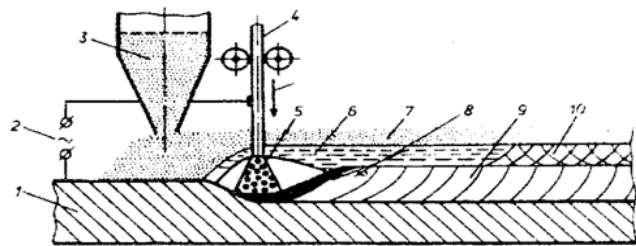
Схема наплавлення під шаром флюсу: 1 – виріб; 2 – джерело живлення; 3 – флюсоживильник; 4 – механізм подачі дроту; 5 – зварювальна дуга; 6 – розплавлений шлак; 7 – шар флюсу; 8 – зварювальна ванна; 9 – наплавлений валик; 10 – шлакова кірка
